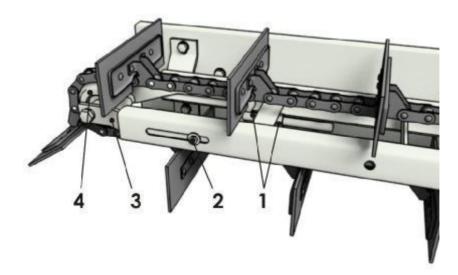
Регулировка натяжения скребковой цепи загрузочного транспортера
